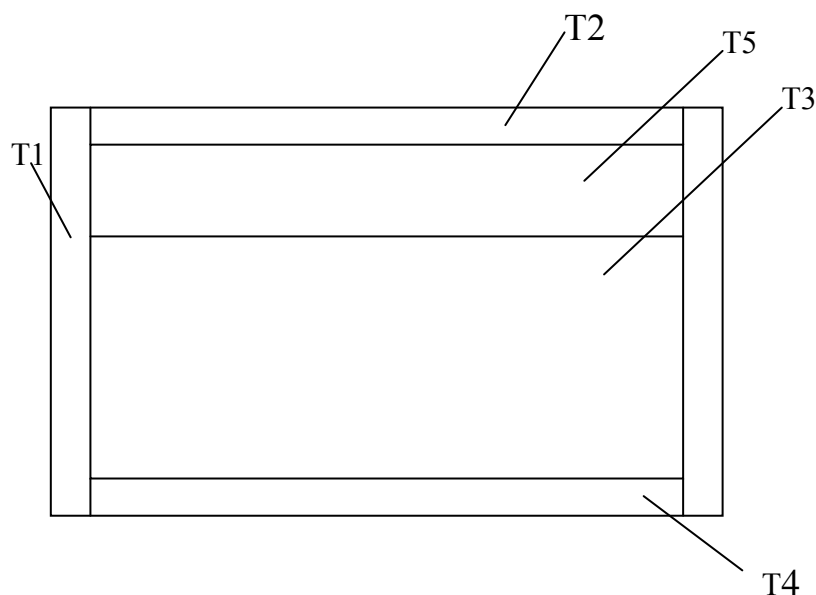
Чертеж корпуса цистерны с обозначенными тепловыми полями
